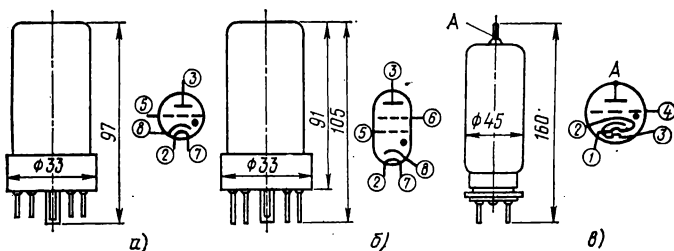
Габаритные чертежи и цоколевка тиратронов:
